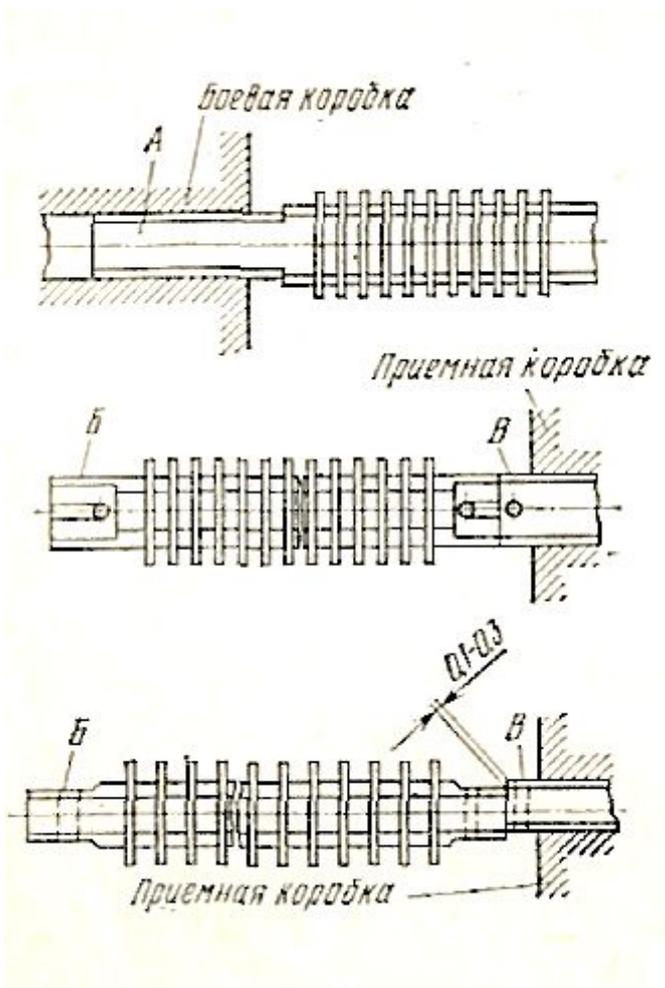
Калибры для наладки и проверки направляющий гребенки батана.
